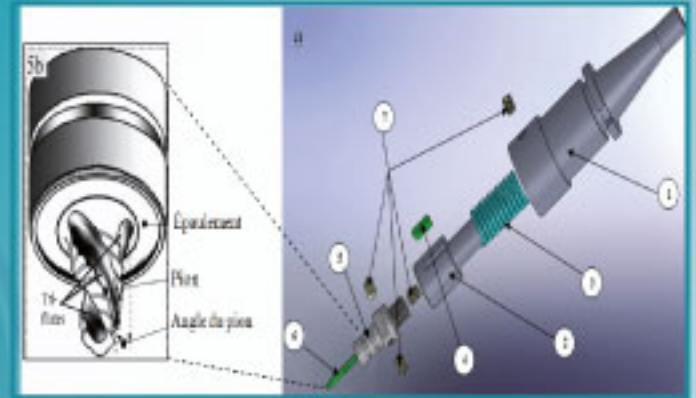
Dessin d'ensemble éclaté de l'outil FSW, (a) Éléments constituant l'outil et (b) Ensemble Epaulement-Pion.
